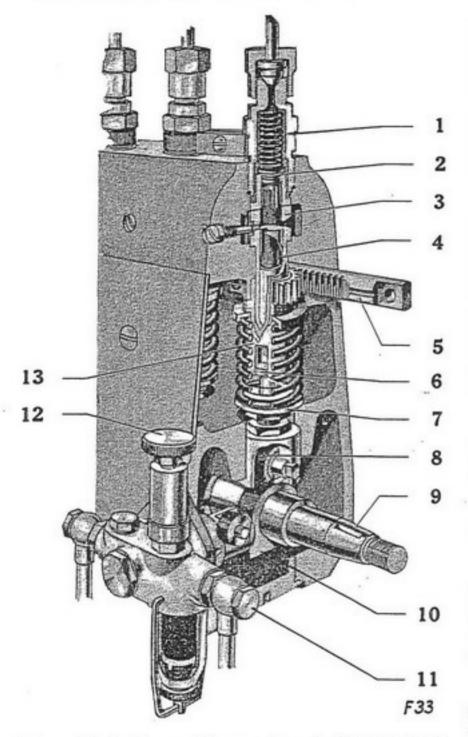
1 - Raccord de pression. 2 - Soupape de refoulement. 3 - Cylindre. 4 - Piston. 5 - Crémaillère. 6 - Queue du piston. 7 - Cuvette
